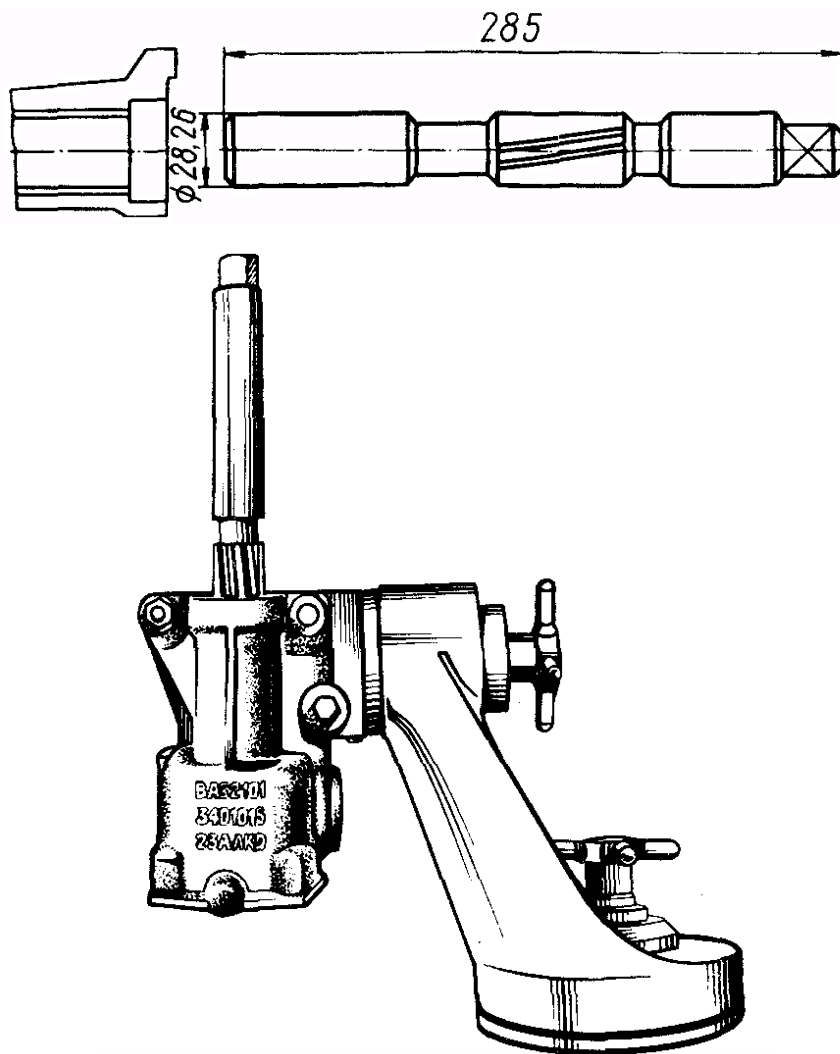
Развертка А.90336 и схема обработки втулки вала сошки
